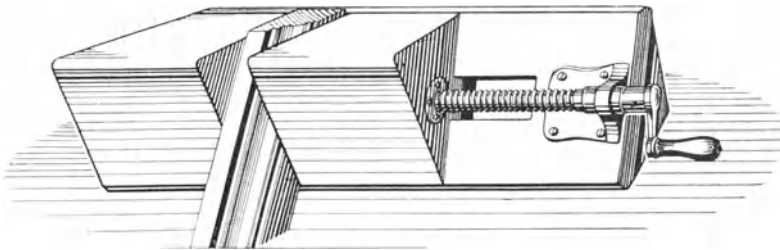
Gehrungsstoßlade zum Schrauben mit eiserner Spindel.
